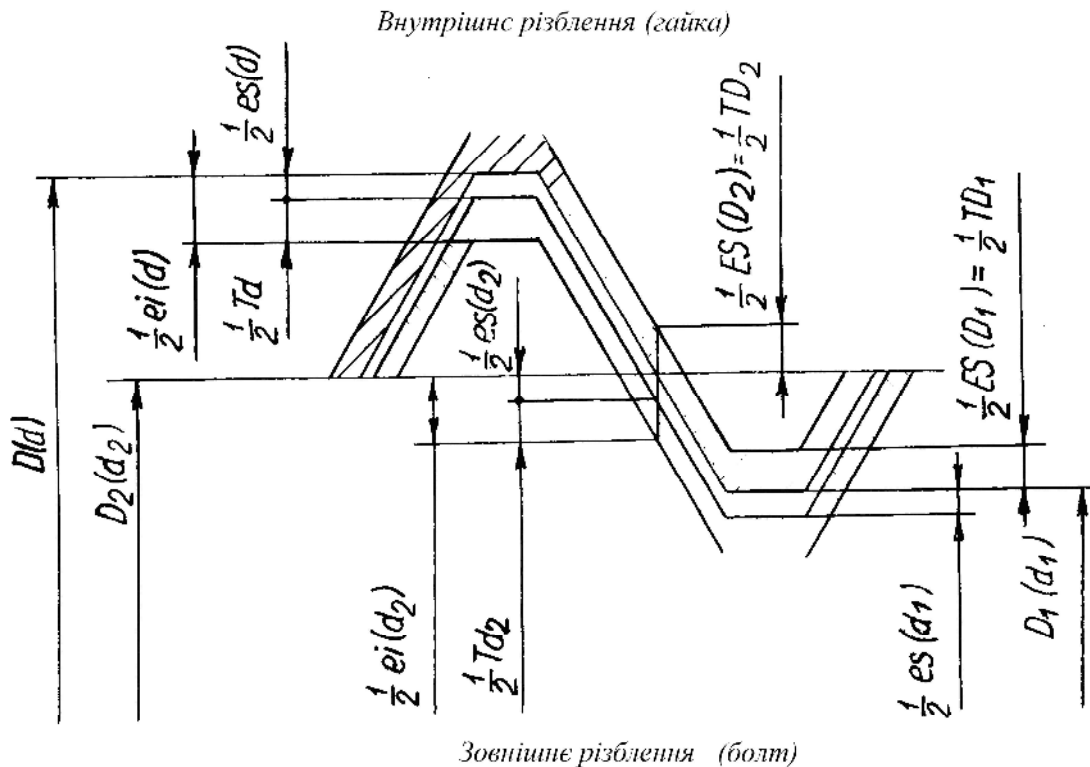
Схема розташування полів допусків різьблення
